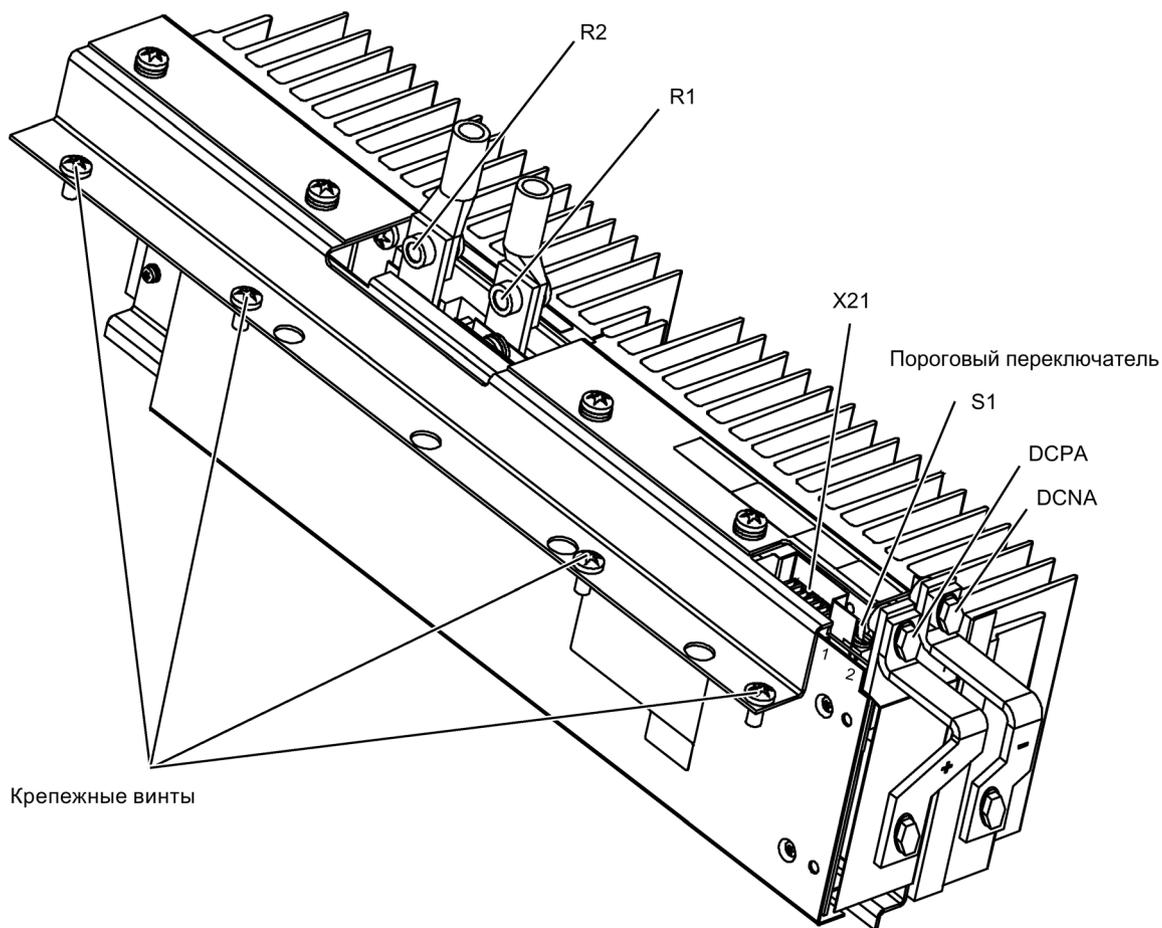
Тормозные модули типоразмеров НХ, JX
